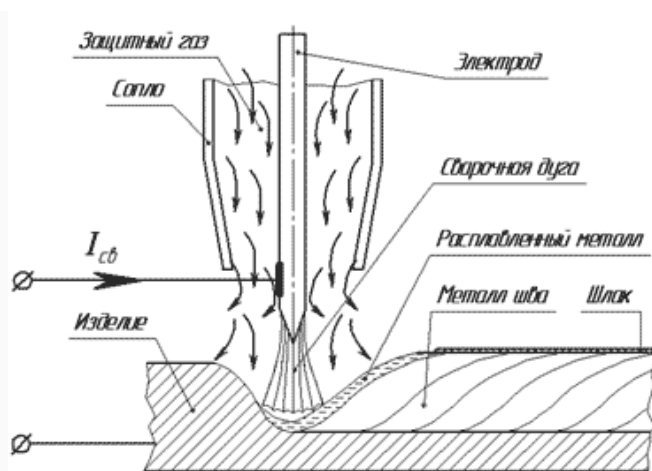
Схема сварки неплавящимся электродом
